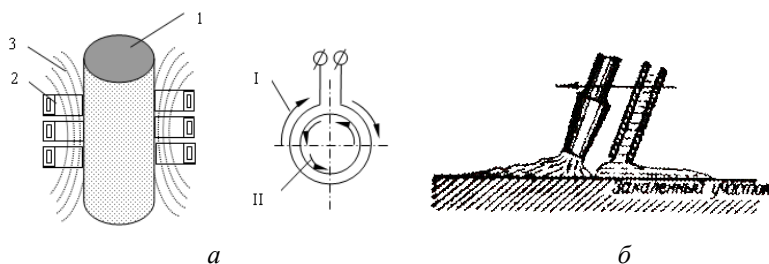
Схема нагрева токами высокой частоты (а) и закалки с помощью газовой горелки (б):
